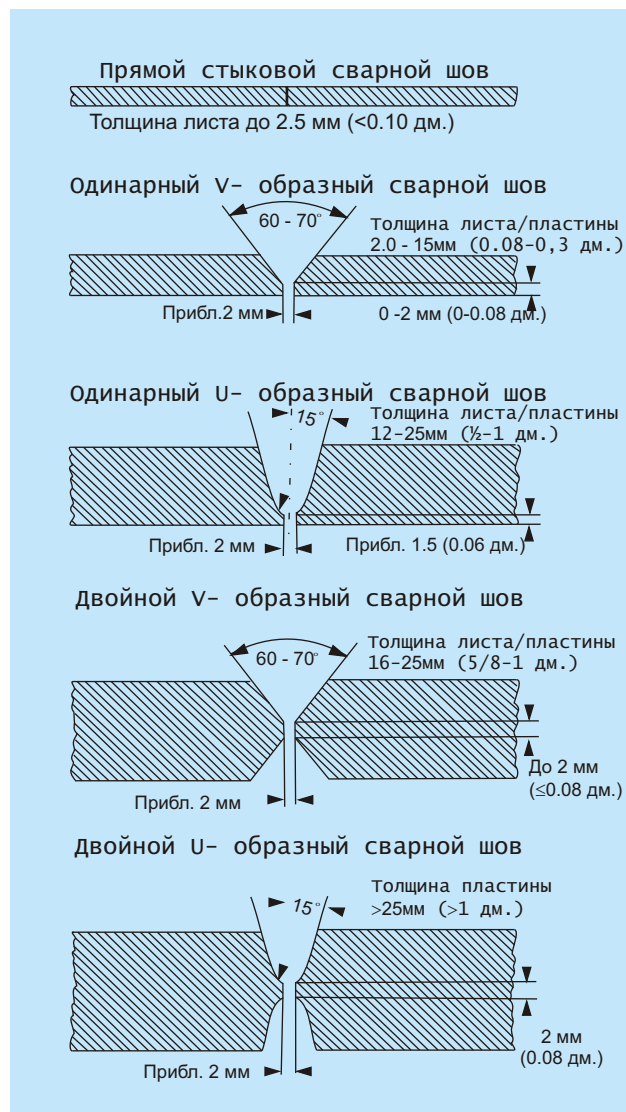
Подготовка кромок для сваривания никелевых сплавов и специальной нержавеющей стали
